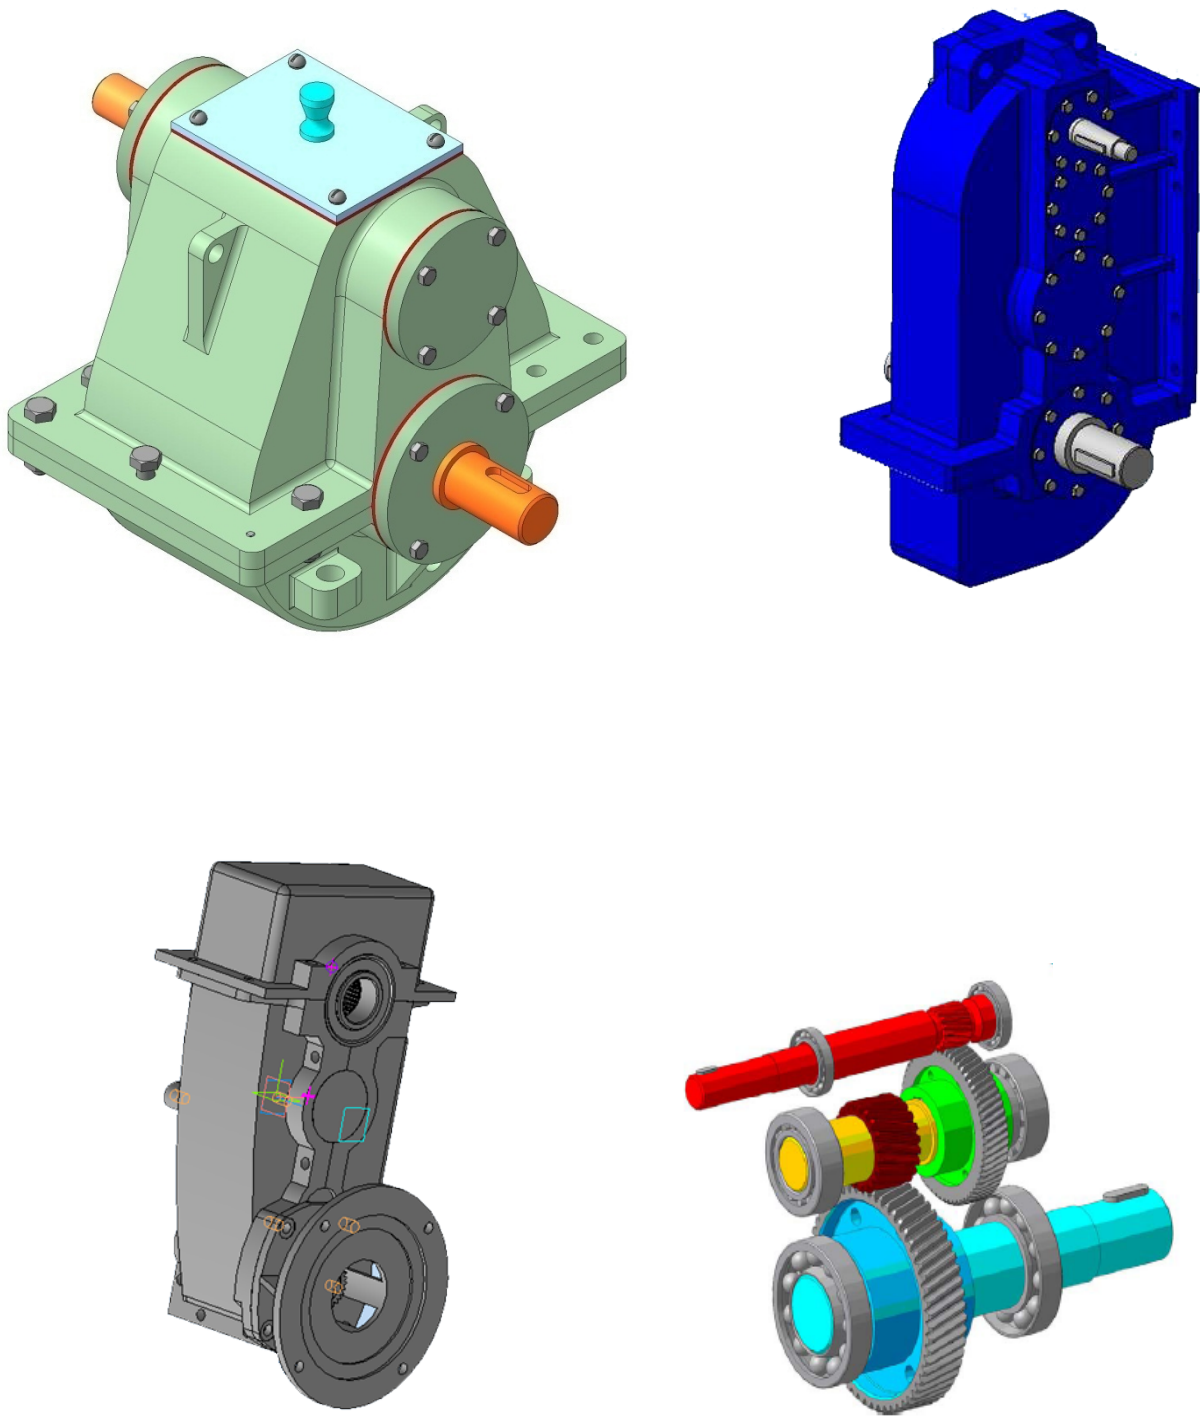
Циліндричний вертикальний редуктор (Ц2В)
